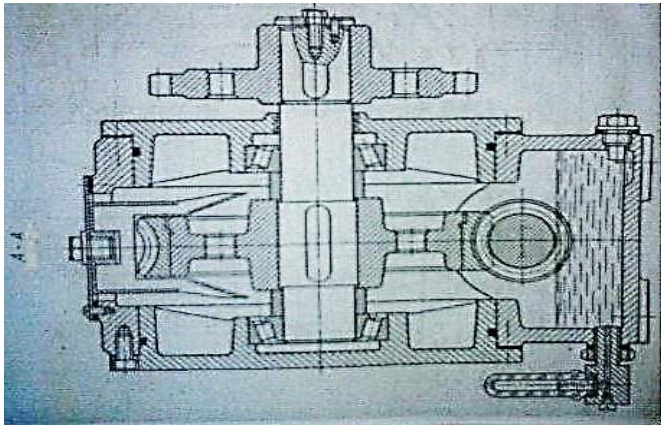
Редуктор черв'ячний одноступінчастий
